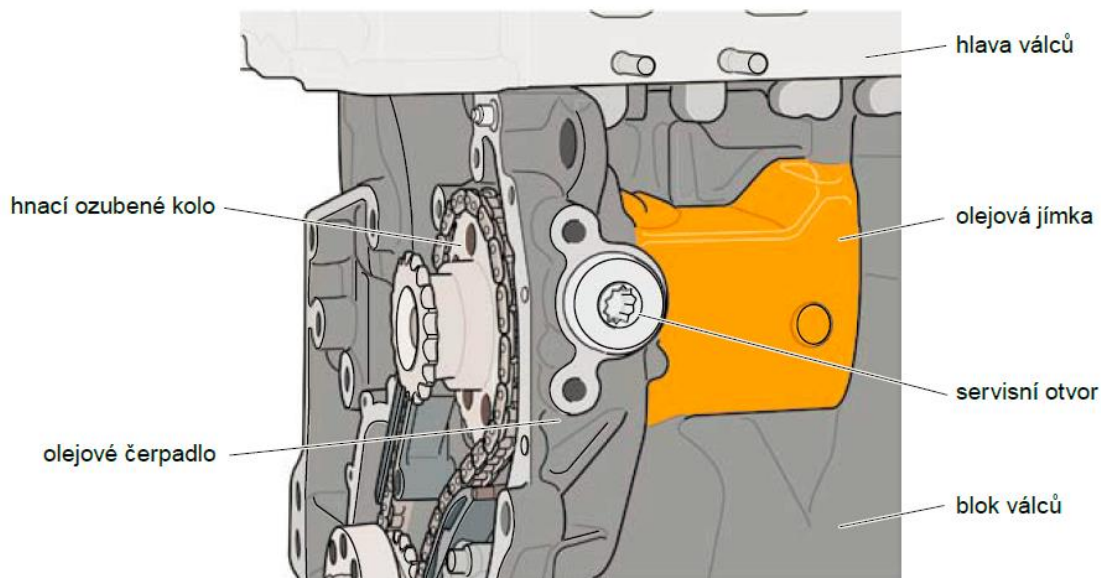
Motor Škody Superb II 3,6 l/191 kW FSI [60]
